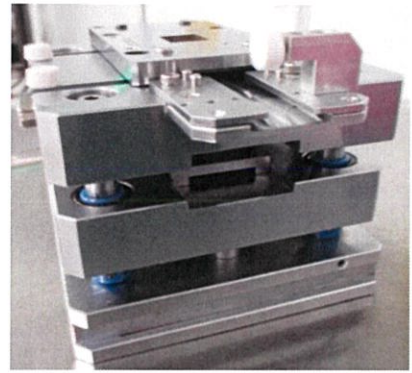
(ข) แสดงด้านหลังของเครื่องมือ Cutting Tool
